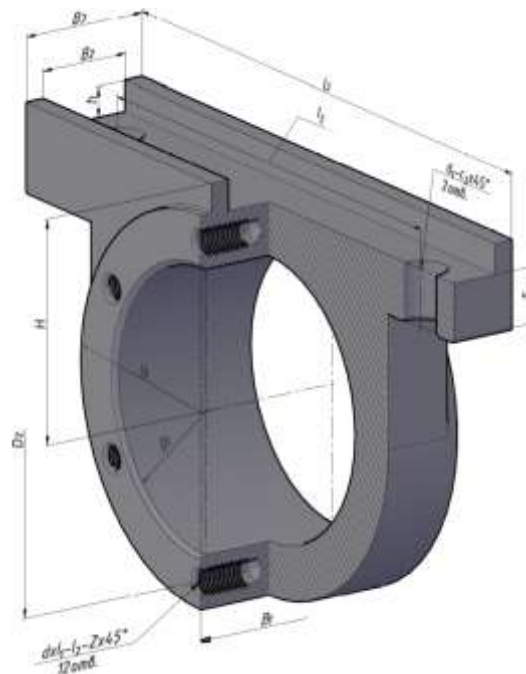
Зображення деталі для виконання робочого кресленника «Корпус»
